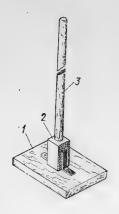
1 — основание; 2 — стойка; 3 — ручка
